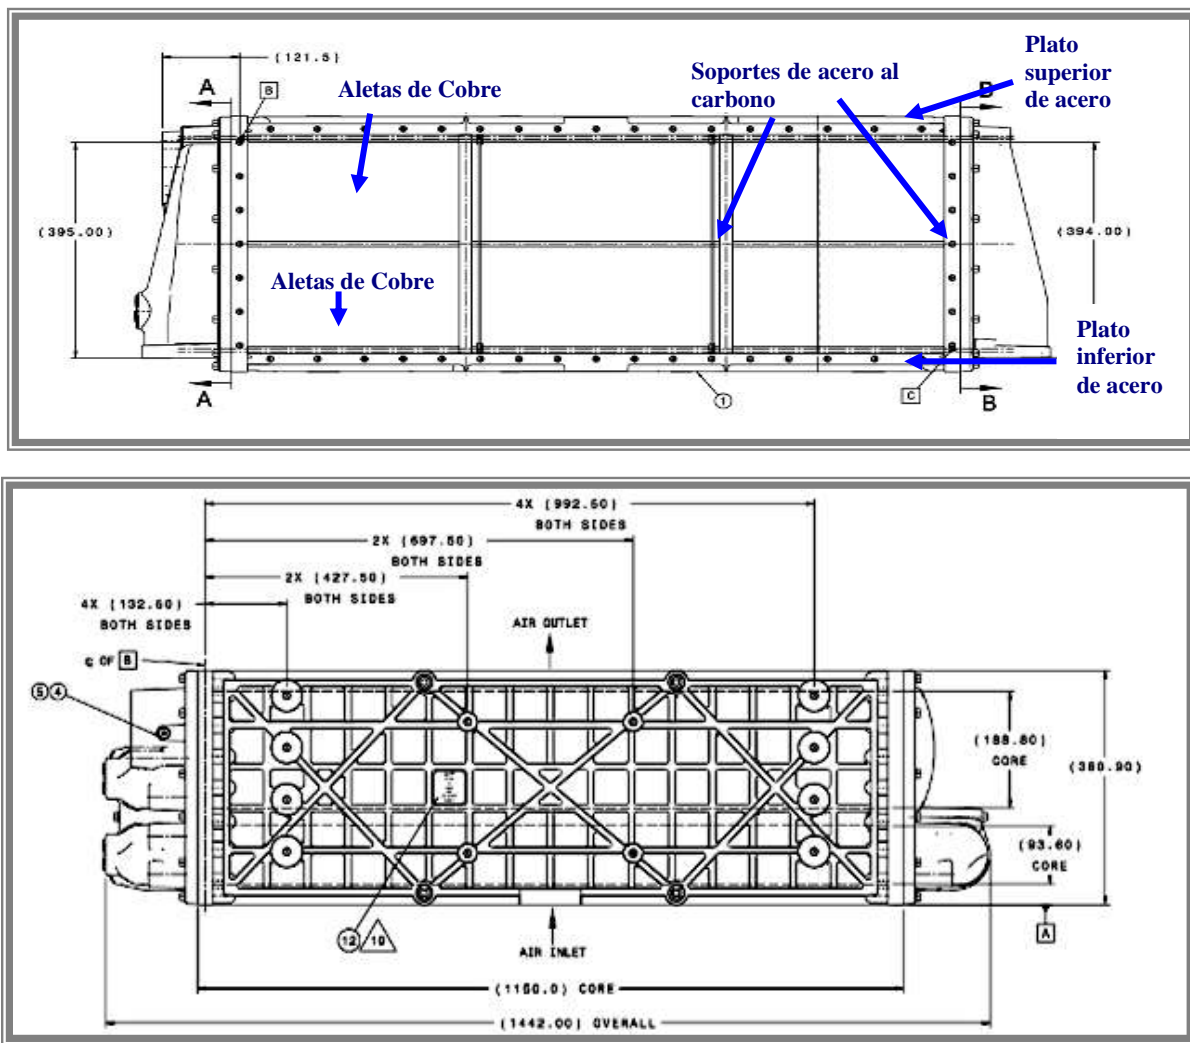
Vista lateral (Figura superior), esta vista se constituye de cobre principalmente, y vista superior del intercambiador de calor (Figura inferior). El plato que se observa, es el plato superior del intercambiador, el cual se construye de acero al carbono.
